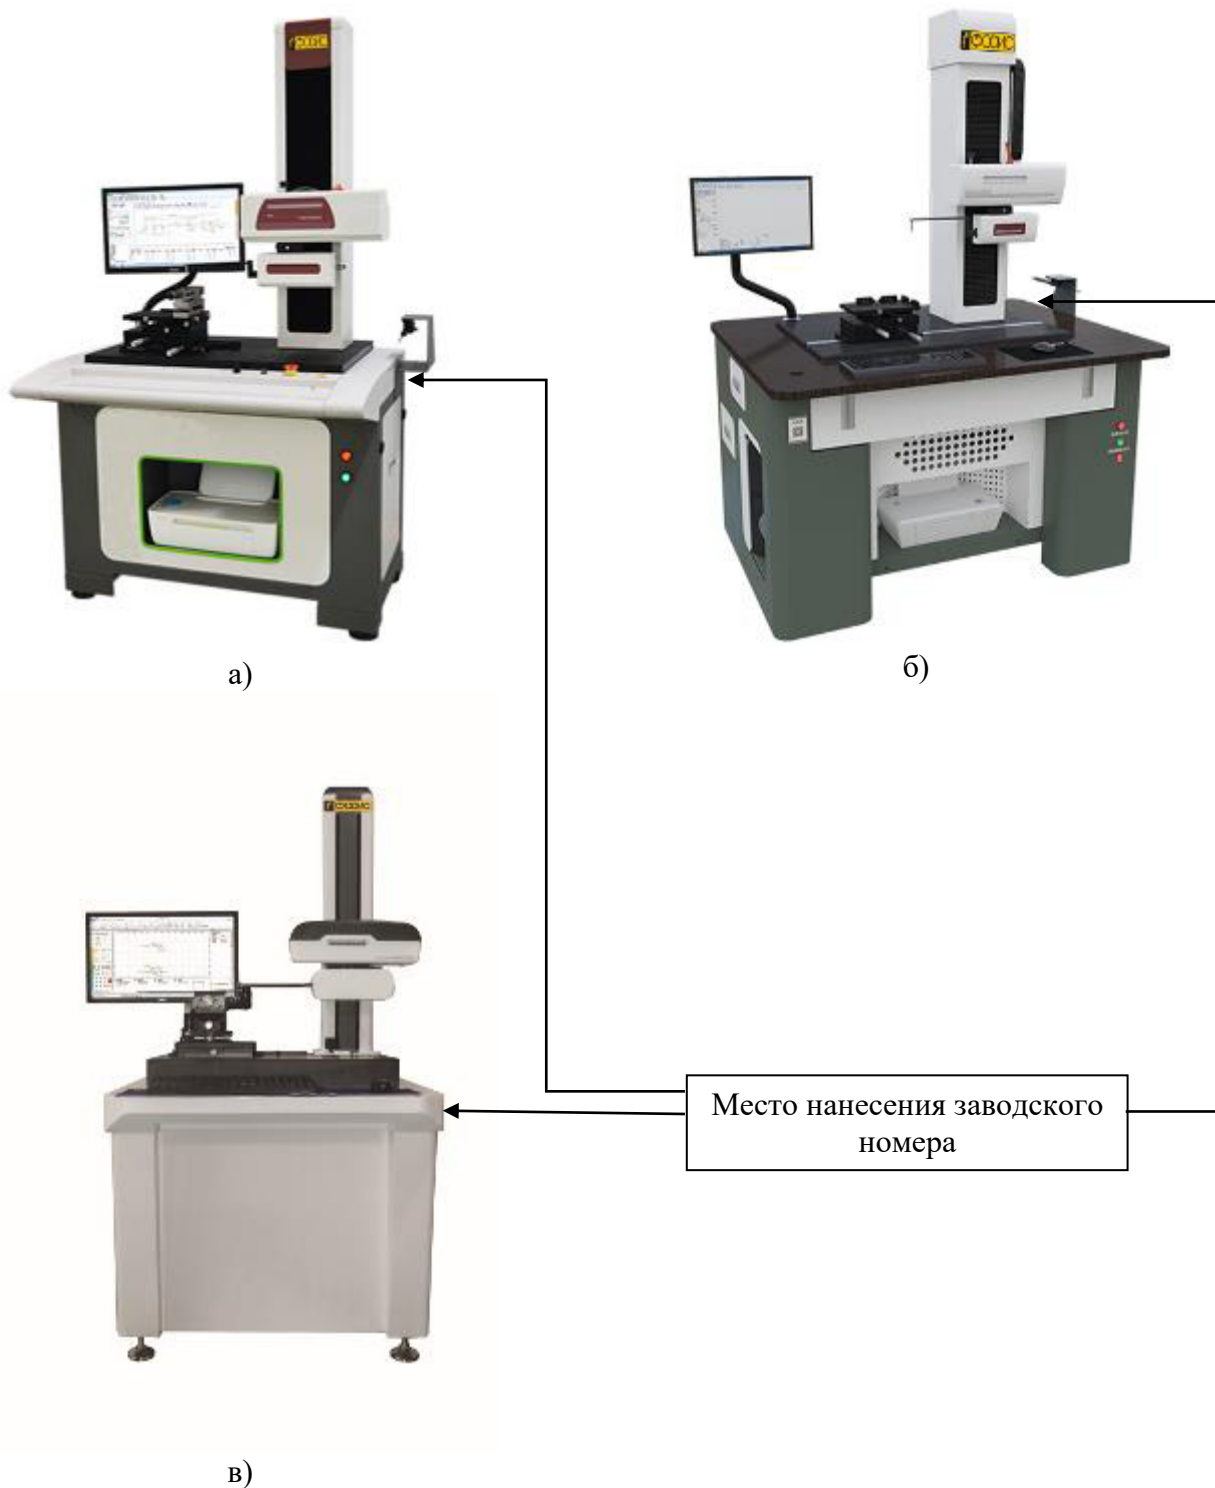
Общий вид приборов для измерений параметров контура и шероховатости поверхности Fodis а) SPR1000; б) SPR2000; в) SPR3000
